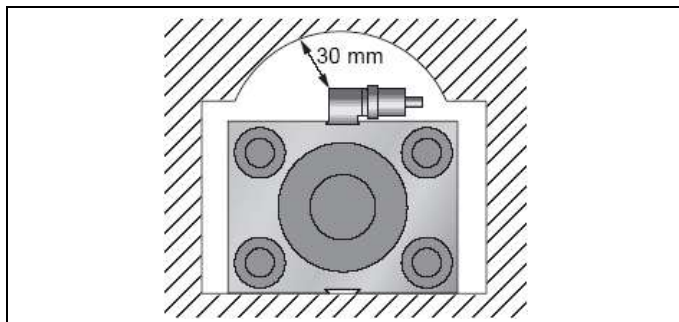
Distanza minima dei sensori rispetto alle protezioni ecc.
